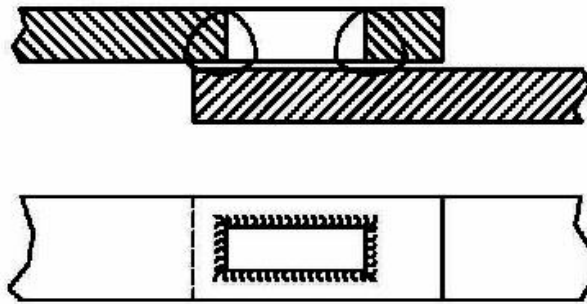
Ejemplo de soldadura de ranura [13]
